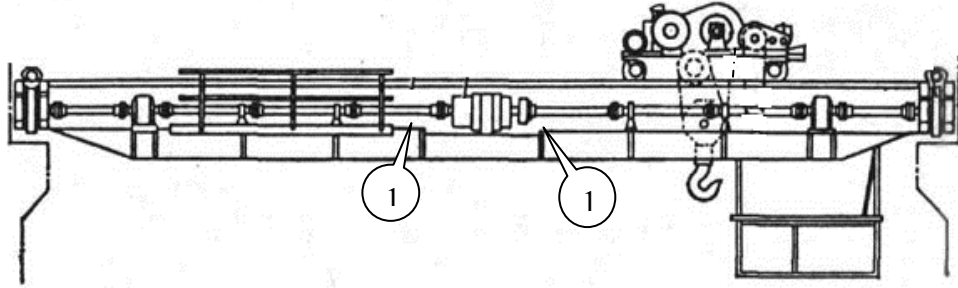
Схема розташування тріщин в металі і зварних швах
